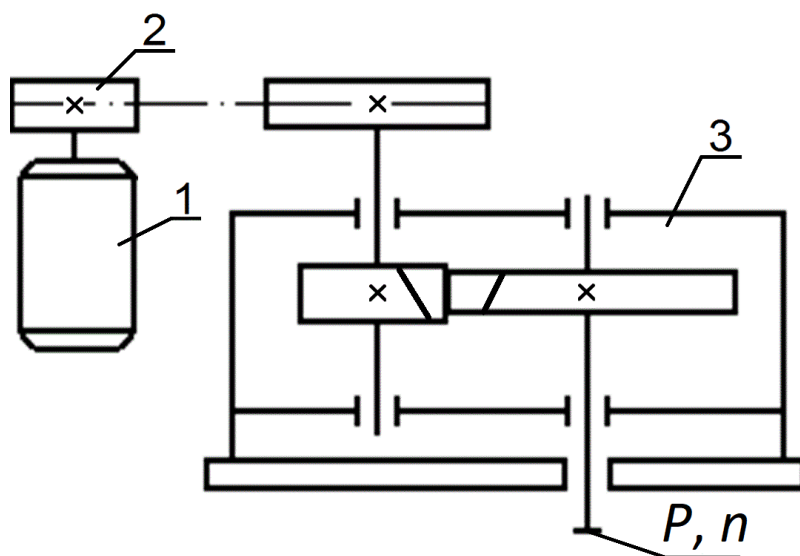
Привод к мешалке: 1 – электродвигатель; 2 – горизонтальная клиноременная передача; 3 – цилиндрический редуктор с косозубой передачей
